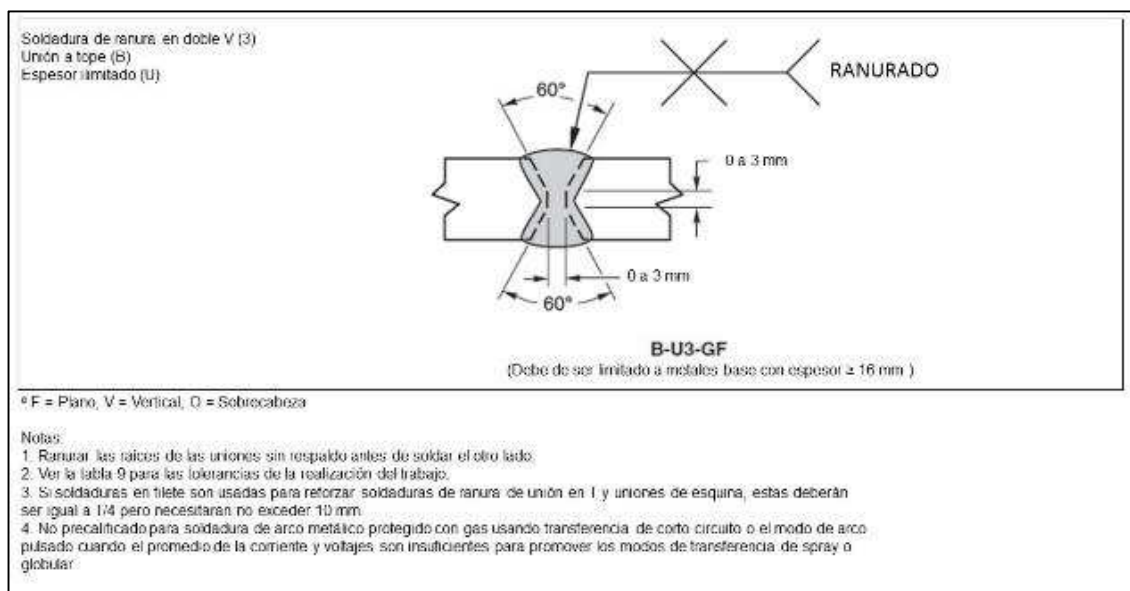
3 Unión en doble V precalificada para penetración completa de soldadura- Proceso de soldadura por arco metálico protegido con gas (14).
